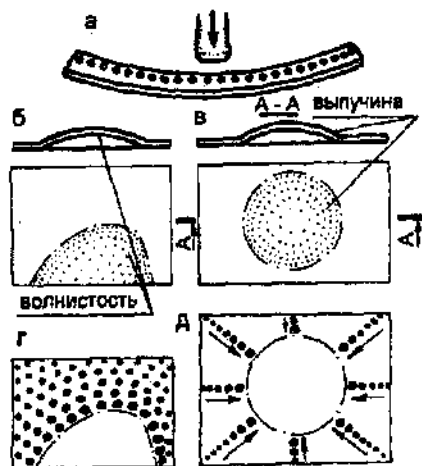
Правка полосы, имеющей серповидную кривизну (а), и схема правки листового металла: б, в — вогнутые заготовки; г, д — распределение ударов
